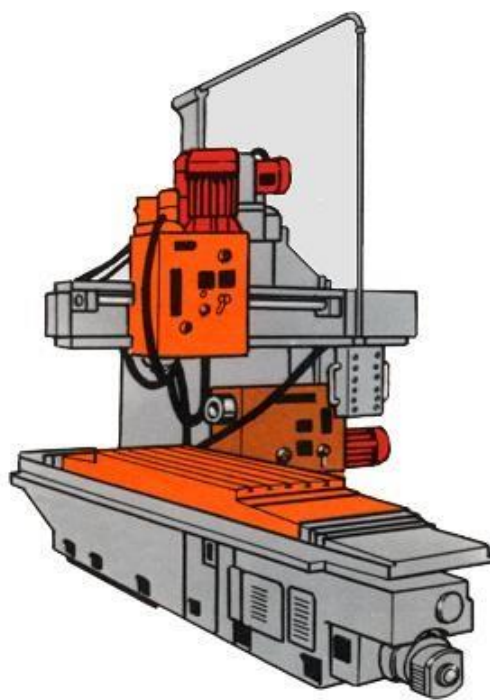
Одностояковий поздовжньо-фрезерний верстат
